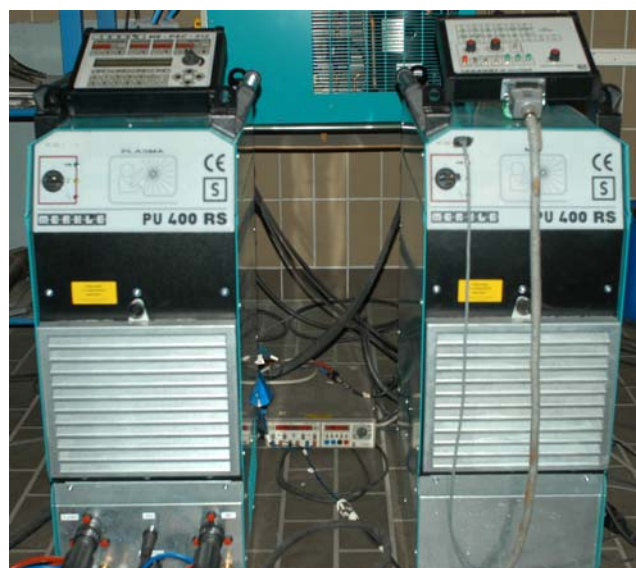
Schweißanlage der Fa.Merkle mit Brenner und Drahtvorschubeinheit
